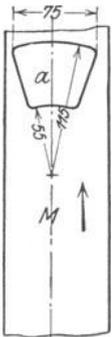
Aufreißen der Zähne zu Abb. 89/90.
